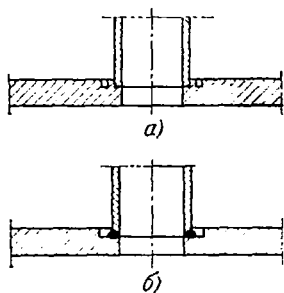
Тавровая сварка тонкой стенки с толстой.
